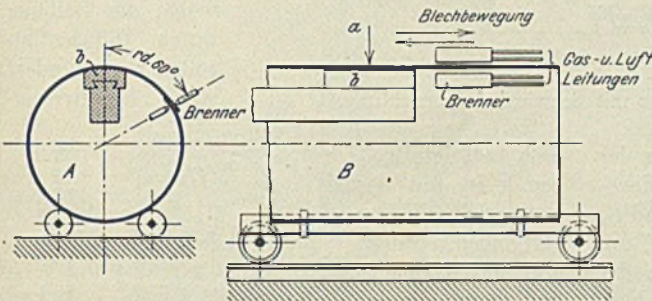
Wassergas-Kesselschweißung.
